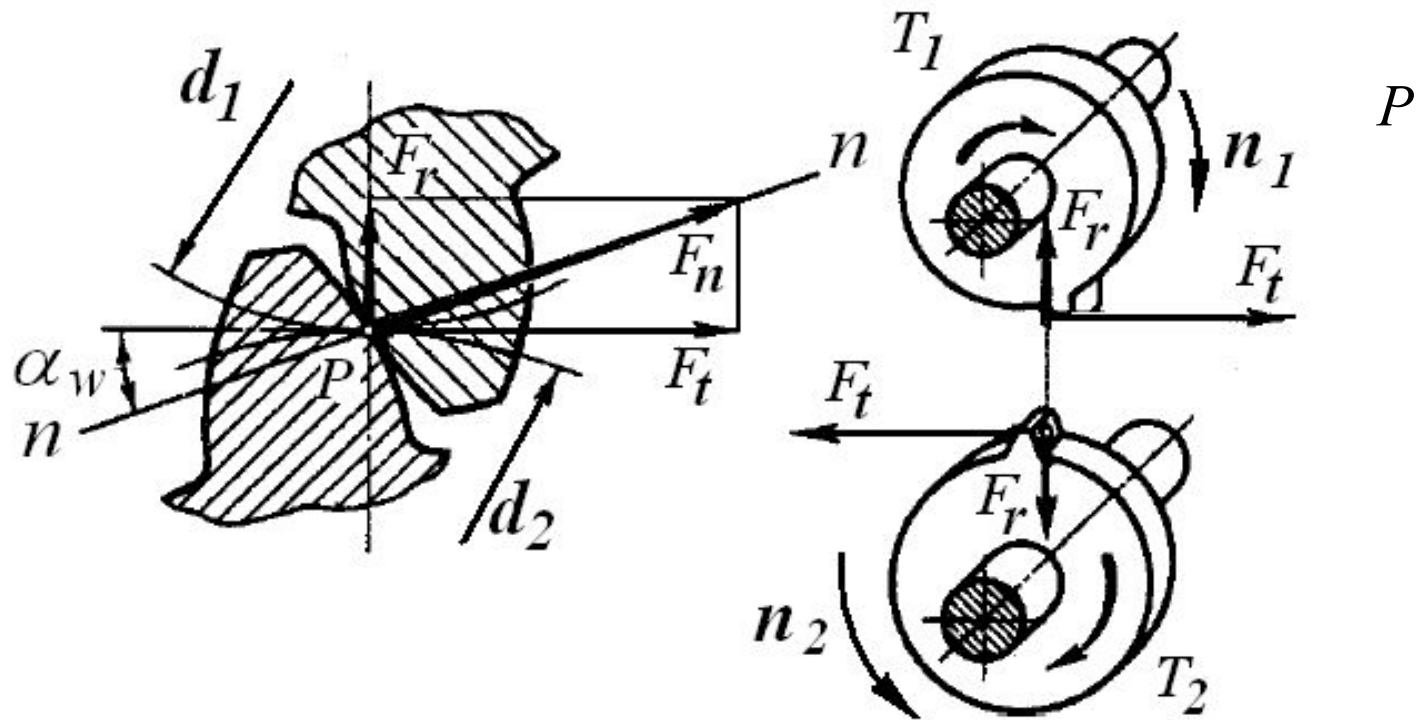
Силы в прямозубой цилиндрической передаче.
